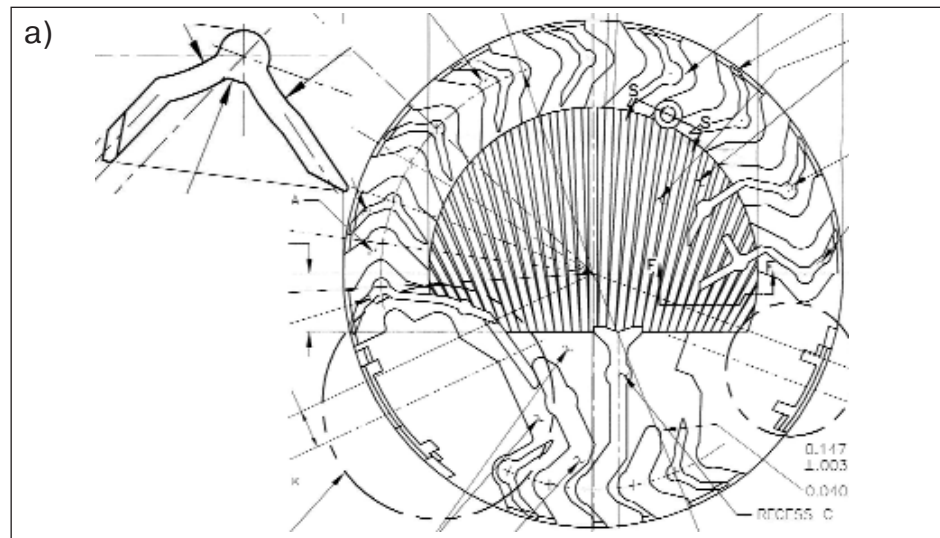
Фрагмент чертежа дымовой камеры адресно-аналогового извещателя
